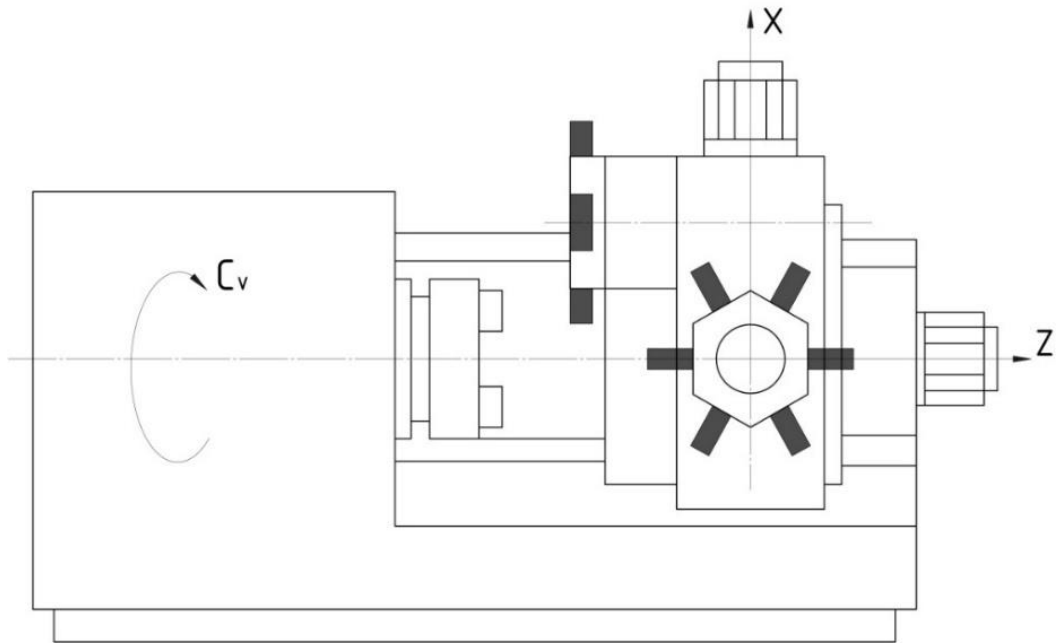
Компонівка токарного верстата (Варіант 3)
